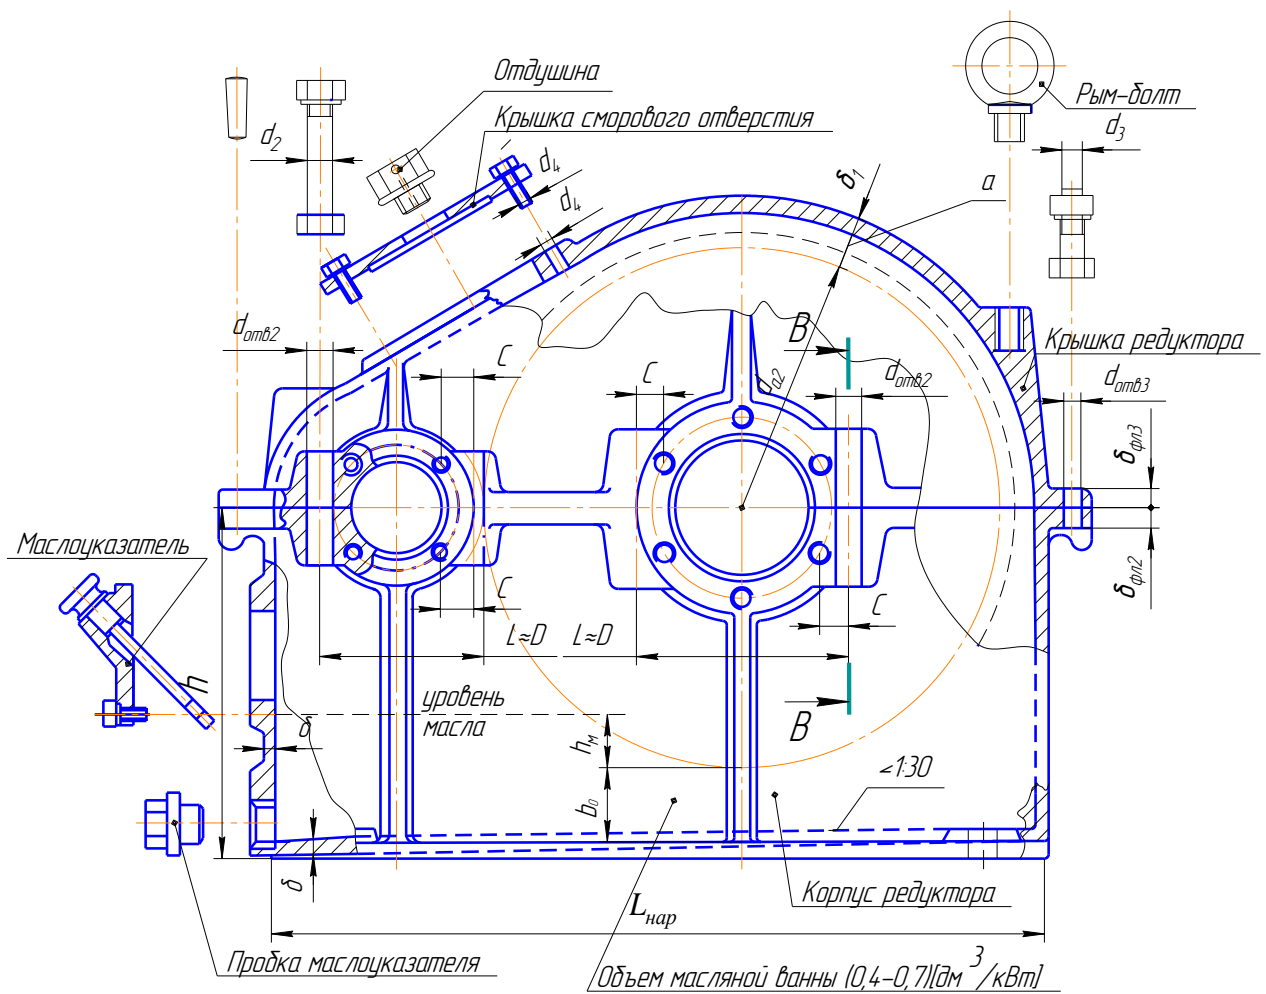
(лист 1, листов 3) Конструкции корпусных деталей цилиндрических редукторов с наружным расположением подшипниковых бобышек
